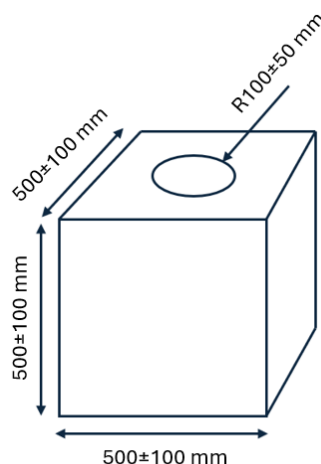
Dimensions générales de l'échantillon / General dimensions of the sample
